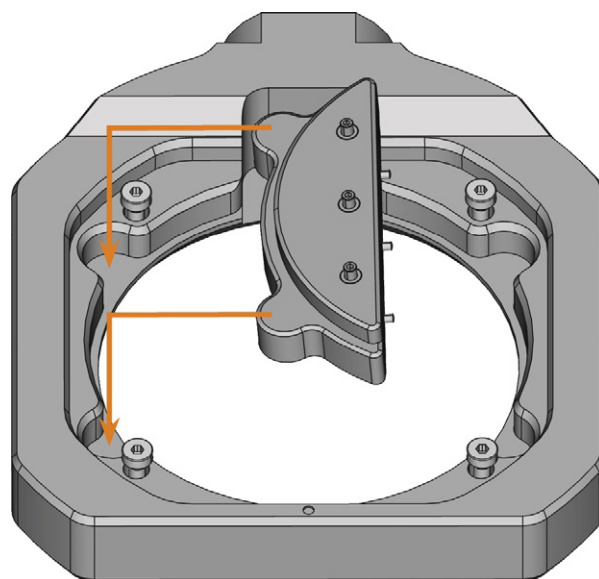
ВСТАВКА ДЕРЖАТЕЛЯ БЛОКА В ДЕРЖАТЕЛЬ
